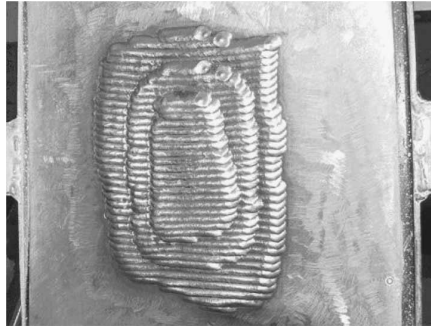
Preenchimento multicamada utilizando solda pelo processo plasma [5]
